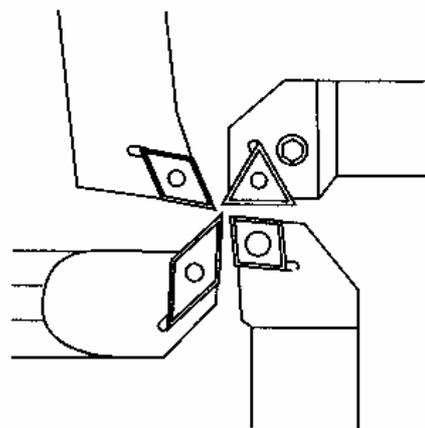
Форма и установка сменных режущих пластин для различных видов точения
